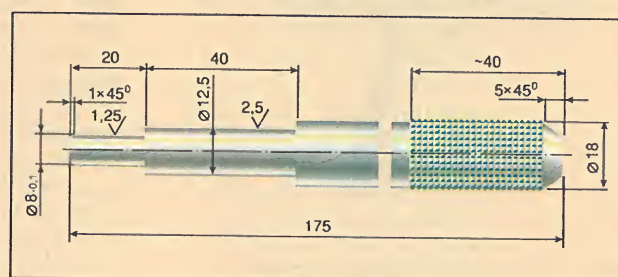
Оправка для запрессовки и выпрессовки направляющих втулок клапанов двигателей ВАЗ-2101...-2108, -21081, -21083, -1111, -11112 и двигателей МеМЗ-245.
